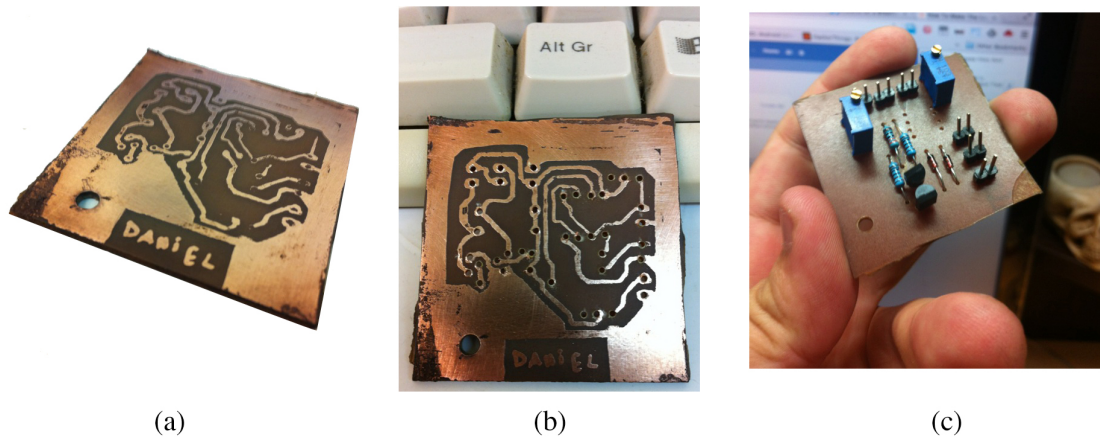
Placa de circuito impresso após a corrosão em (a) e (b), em (c) a placa após ter os componentes soldados.
